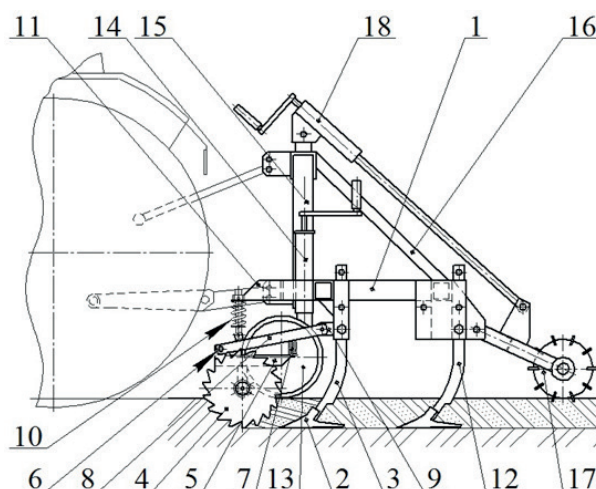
Конструктивная схема культиватора виноградникового, вид сбоку: 1 – рама; 2 – лапа; 3, 12 – стойка; 4 – зубчатый дисковый нож; 5 – корпус; 6 – шарнир; 7 – пружина автоколебаний; 8 – рычаг; 9 – держатель; 10 – нажимная пружина; 11 – кронштейн; 13 – опорное колесо; 14 – механизм регулирования рамы; 15 – навеска; 16 – растяжка; 17 – прикатывающий каток; 18 – винтовой механизм
